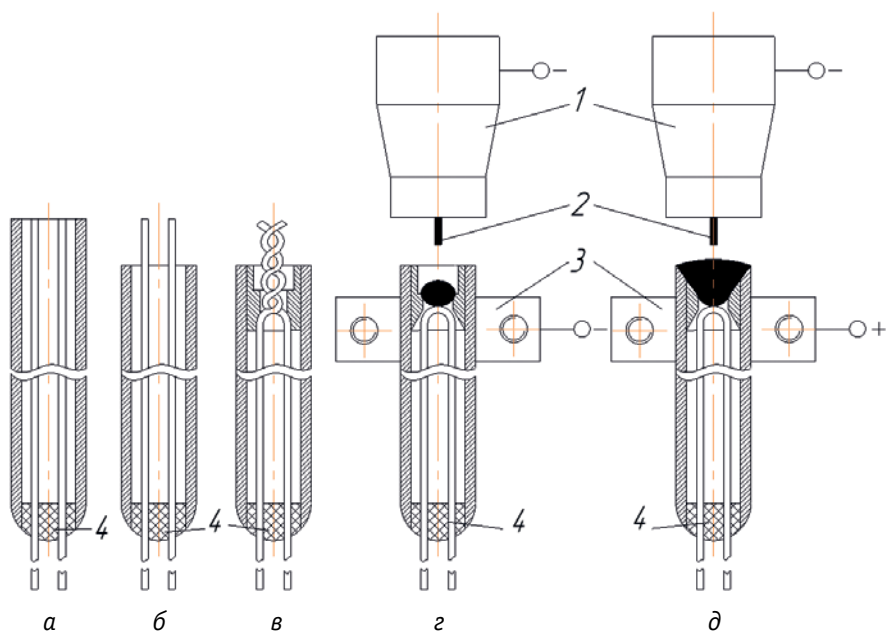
Последовательность подготовки и сварки рабочих спаев термопар диаметром 3–6 мм с рабочим спаем, заземленным на оболочку: а – обрезка заготовки; б – освобождение термоэлектродов; в – удаление изоляции, скручивание термоэлектродов и установка пробки; г – оплавление термоэлектродов; д – сварка (1 – горелка; 2 – электрод; 3 – медные губки; 4 – герметик)
